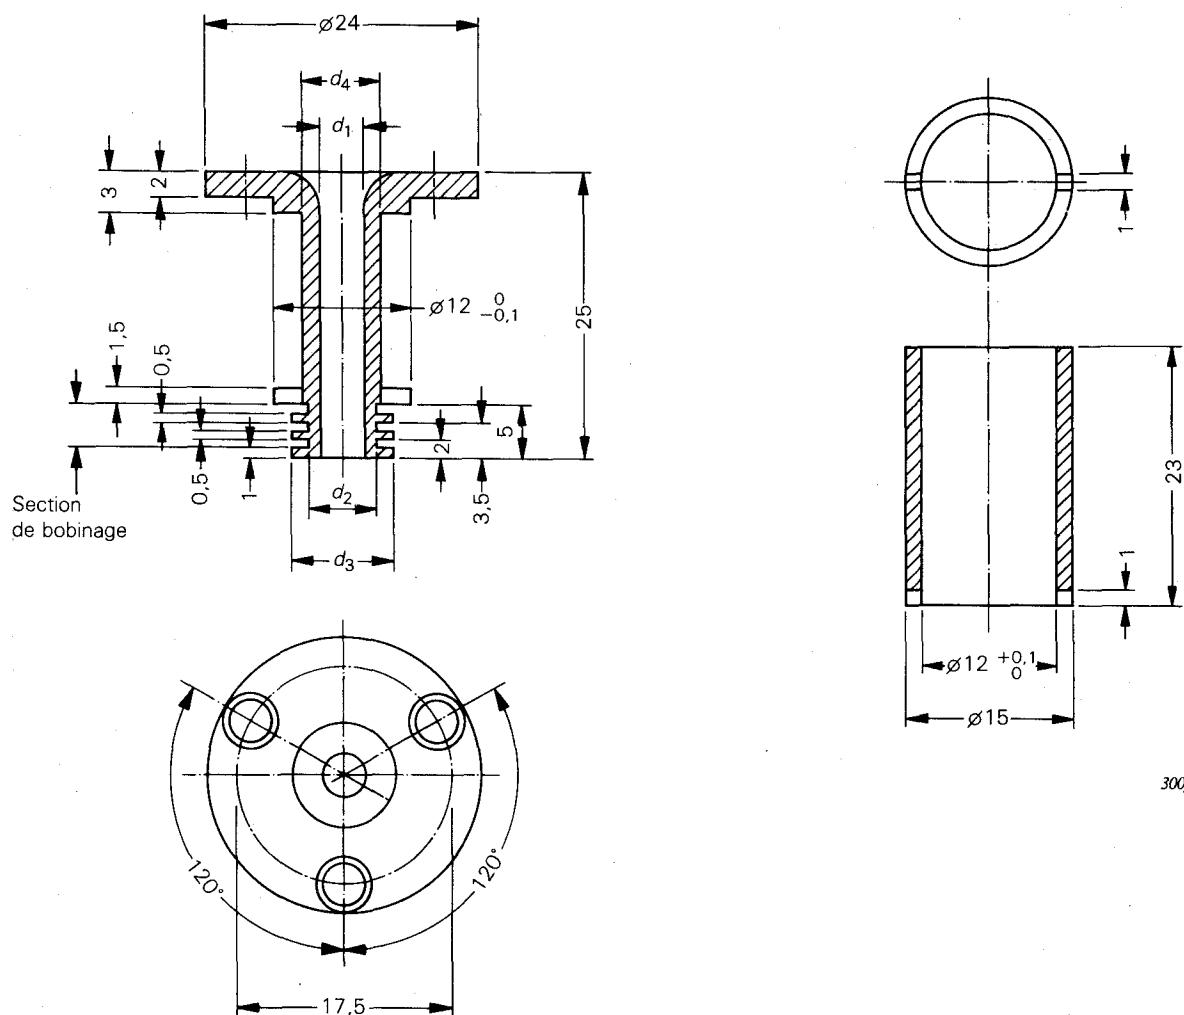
Mandrins de bobinage et tube protecteur (dimensions en millimètres).
